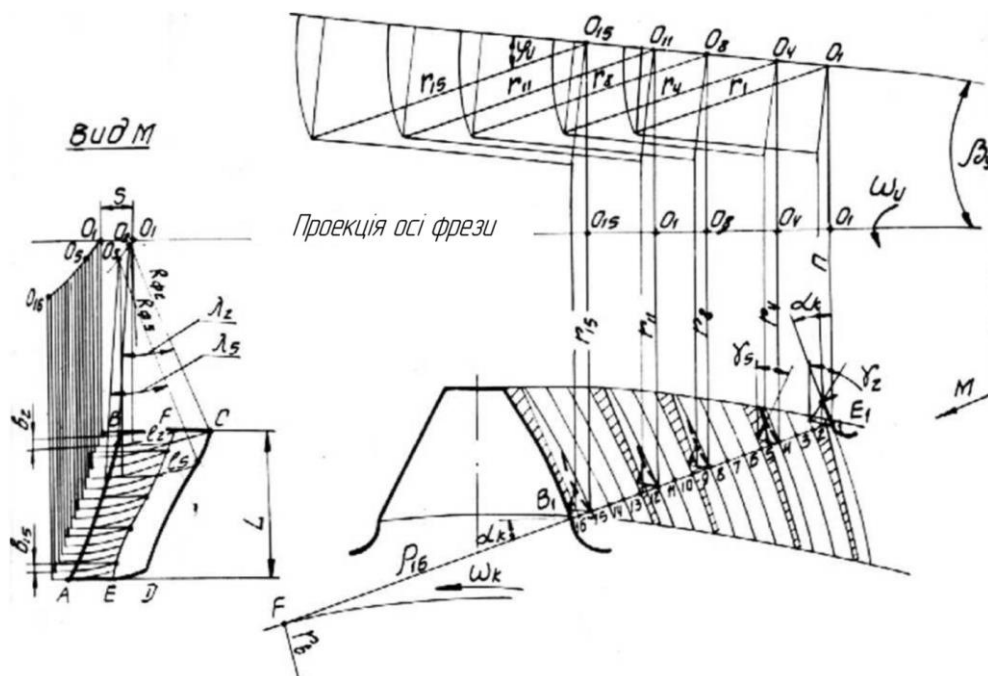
Графічний спосіб побудування контактної області різання правого корпусу черв'ячної фрези з роздільною схемою формоутворення
